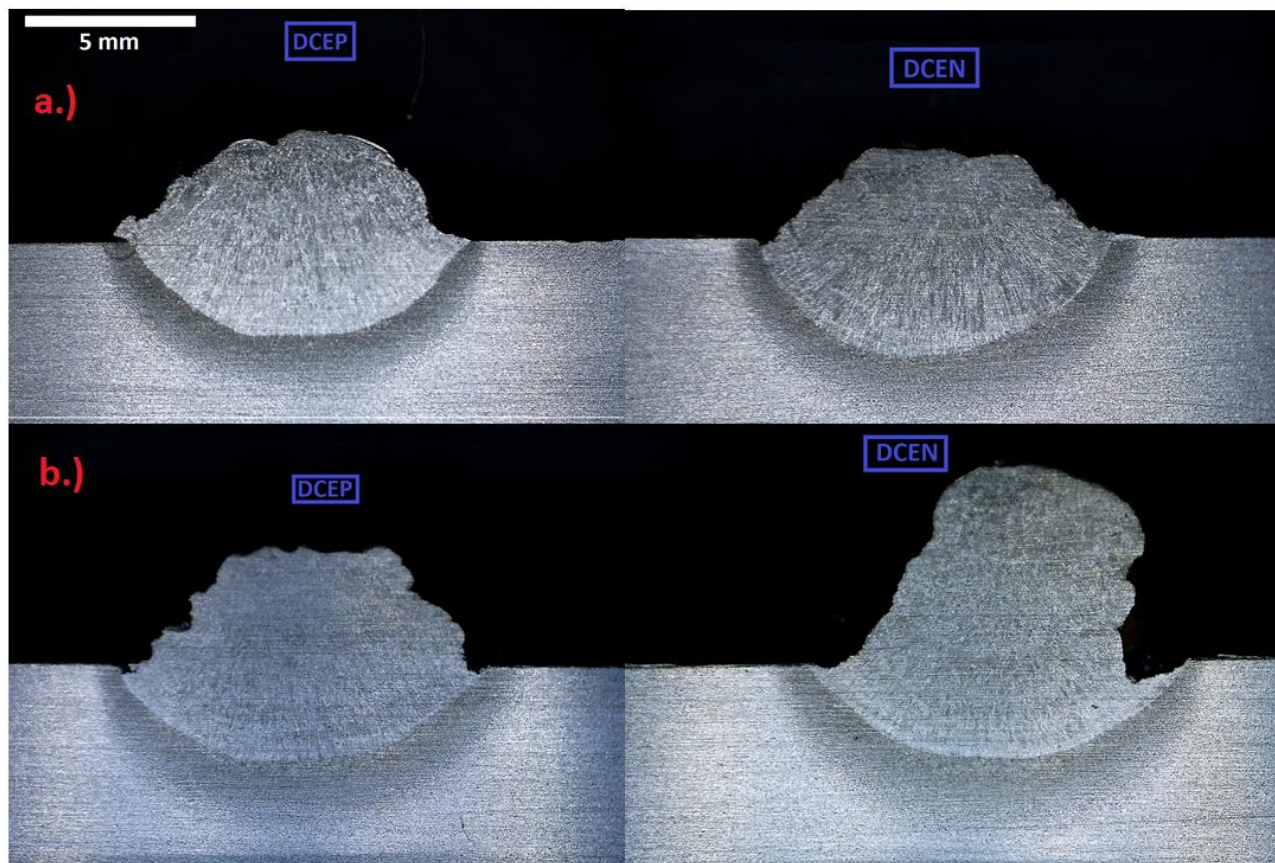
Seções transversais dos cordões de soldadura (a) arame de base oxidante (b) arame de base rutilica
